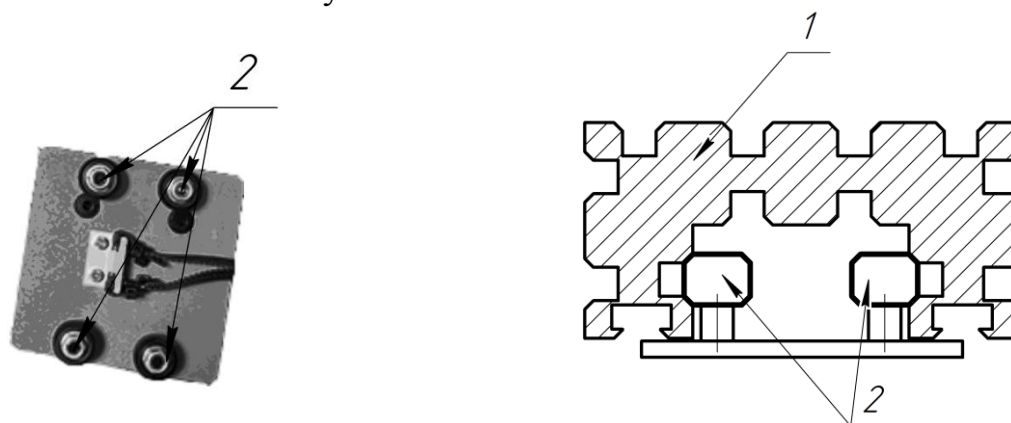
Конструкция каретки и схема зацепления роликов.
